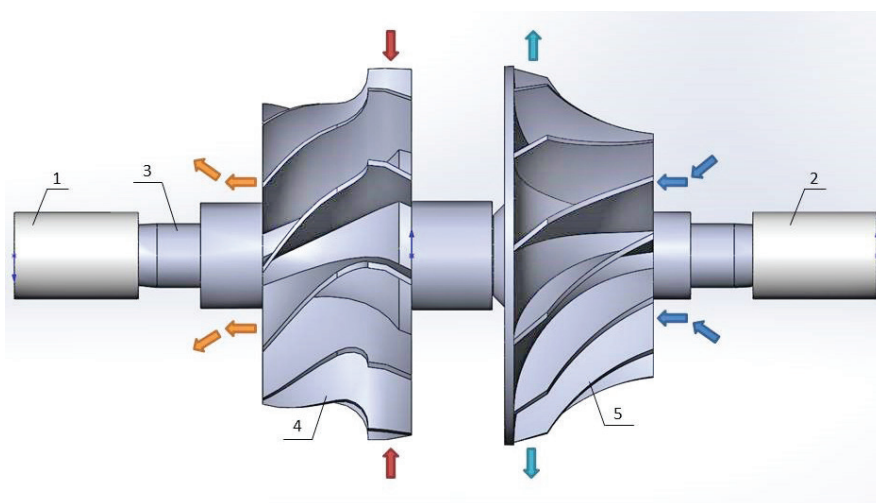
Геометрическая модель для расчета температурных деформаций системы «подшипники - ротор» турбоагрегата: 1 — подшипник со стороны турбины; 2 — подшипник со стороны компрессора; 3 — ротор; 4 — колесо турбины; 5 — колесо компрессора
